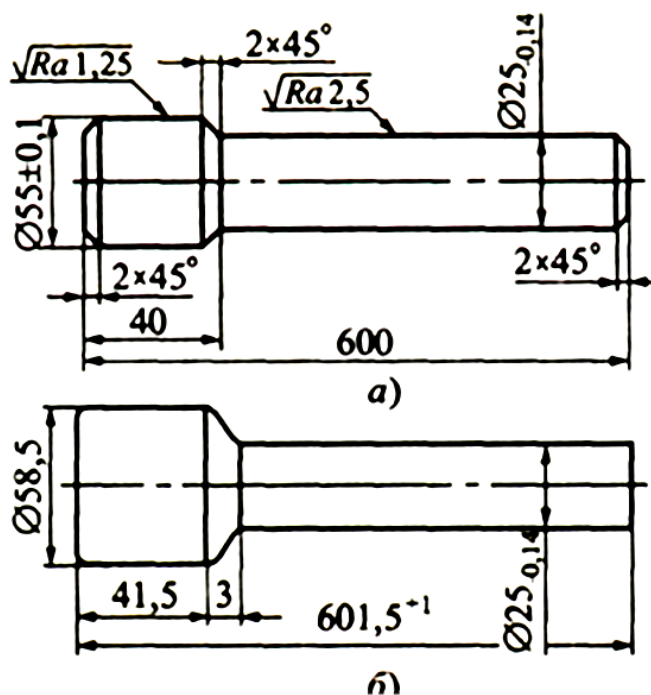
Типовая деталь «Шток» и штампованная заготовка после электровысадки: а- чертёж детали «Шток»; б- чертёж штамповки.
